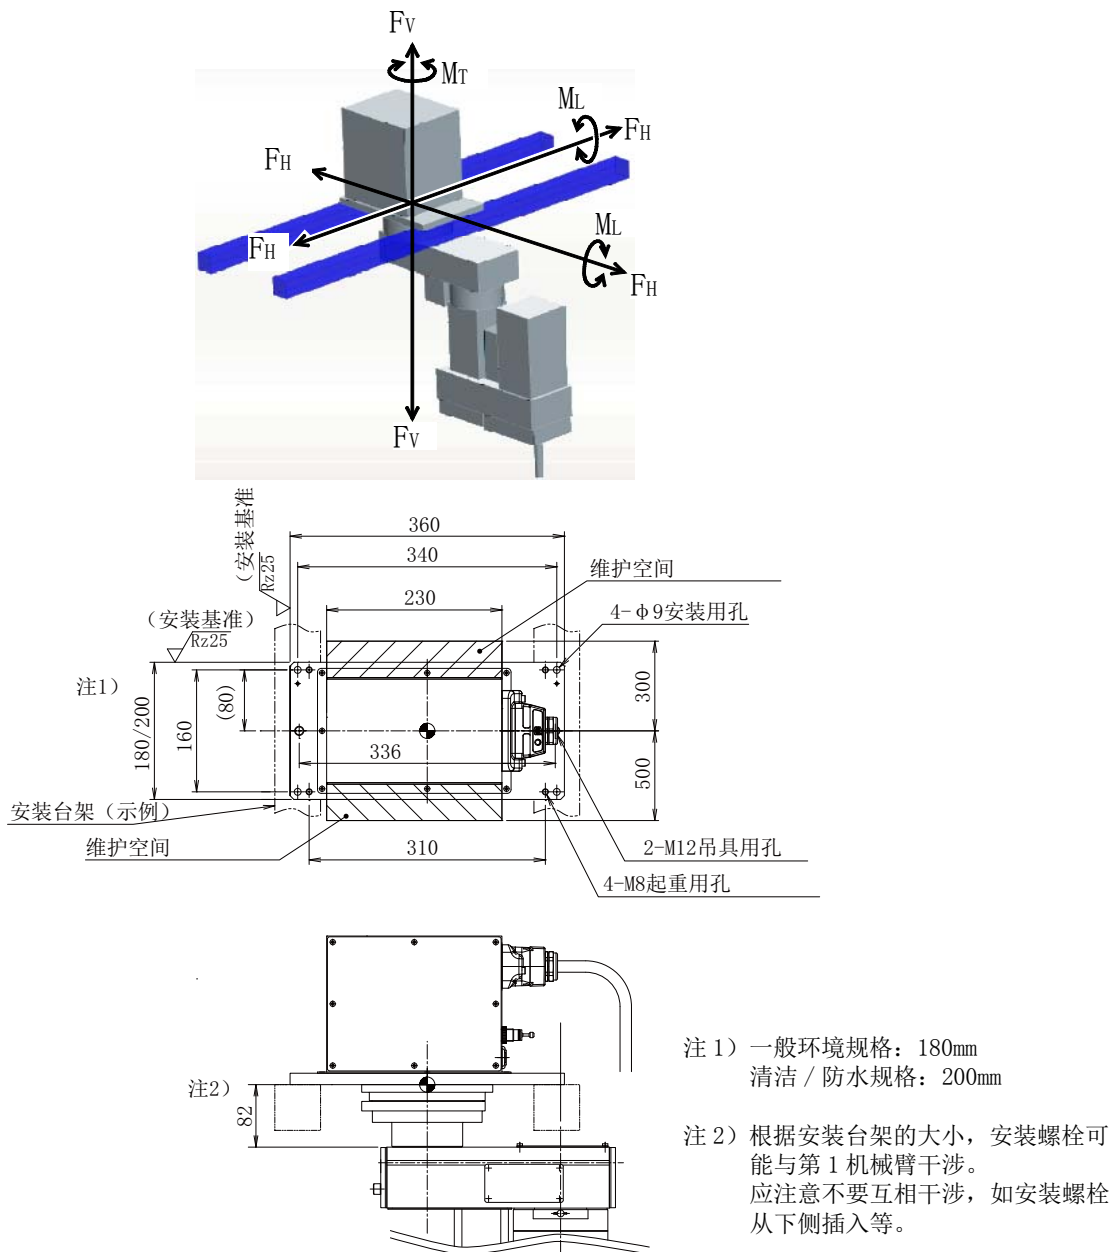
安装尺寸 (RH-3FRHR 系列)
